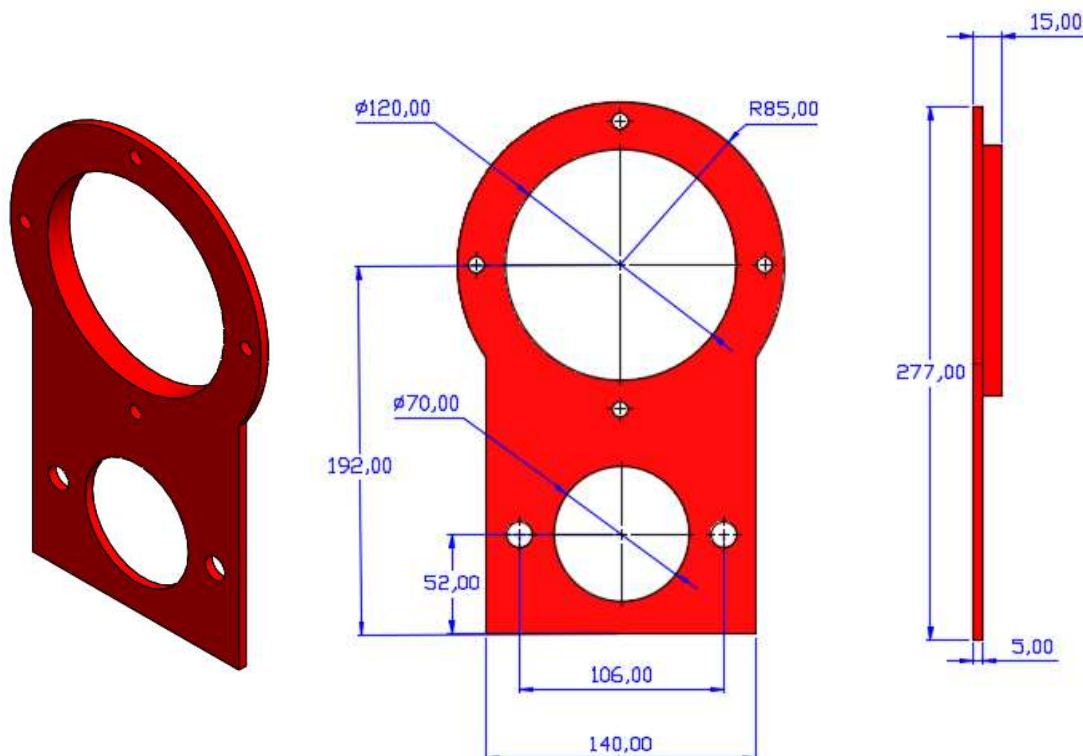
Vista 3D y dimensiones de la placa soporte del motor hidráulico.
